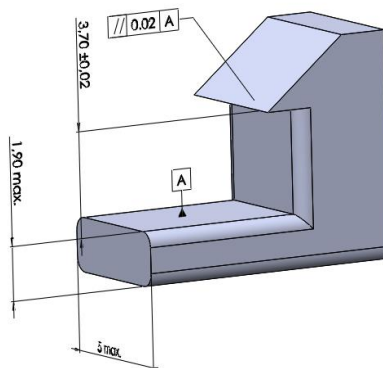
Zadane dimenzijske i geometrijske tolerancije Vrata prednjeg držača
